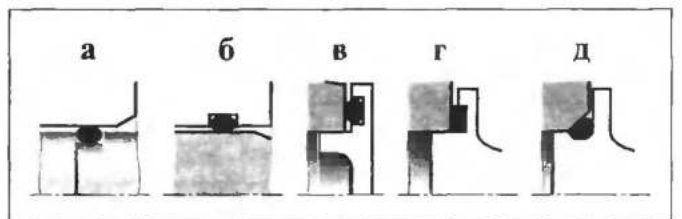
Типовые уплотнения деталей с помощью резиновых колец: а — по цилиндрической поверхности с размещением кольца в канавке внутренней детали; б — то же, но канавка выполнена в отверстии наружной детали; в — уплотнение кольцом круглого сечения по торцу; г — то же, но кольцо имеет прямоугольное сечение; д — уплотнение по фаске
